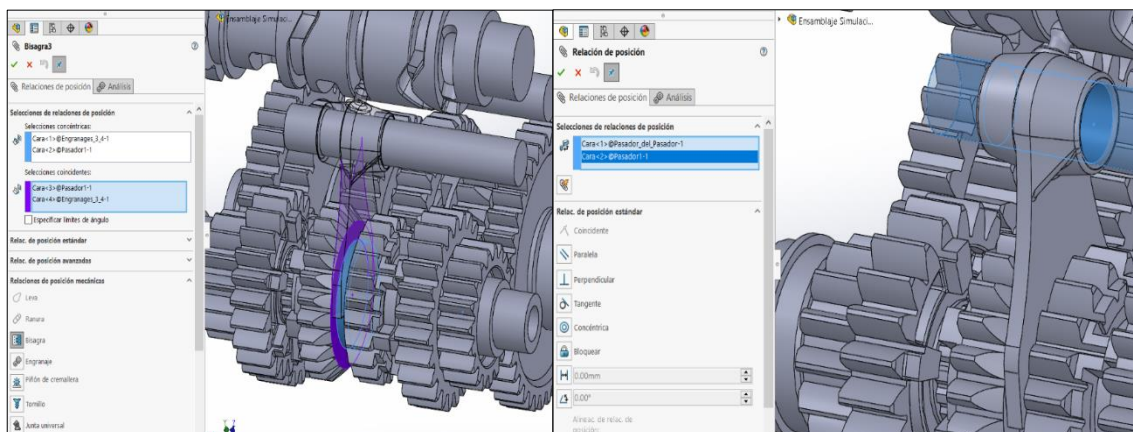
Definición de relación de posición mecánica de engranaje (Fuente: propia)
